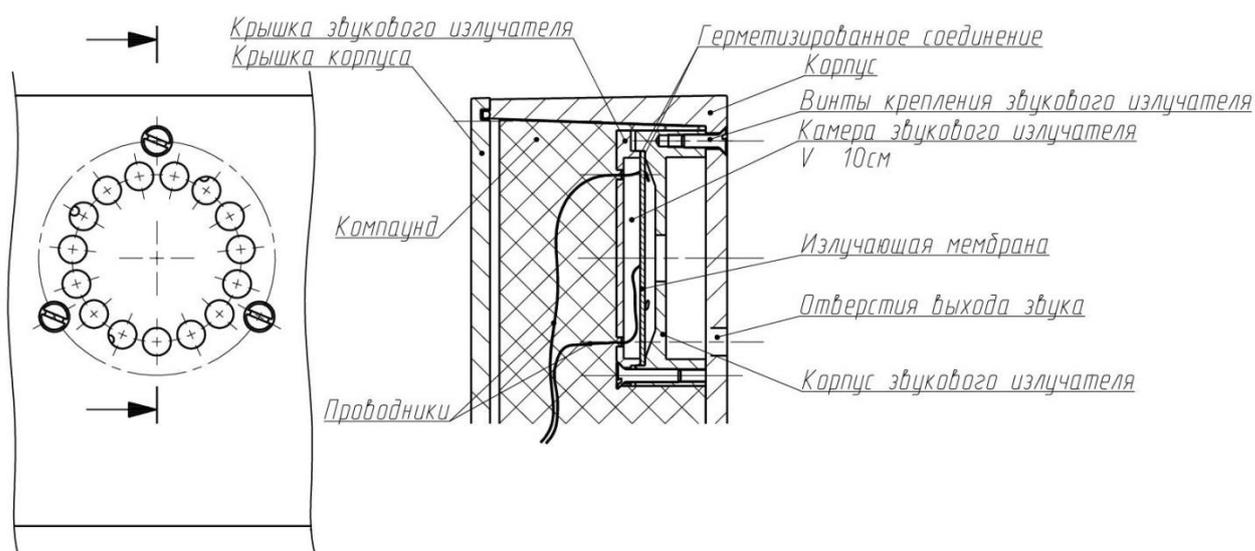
Чертеж взрывозащиты звукового излучателя комбинированных Табло
